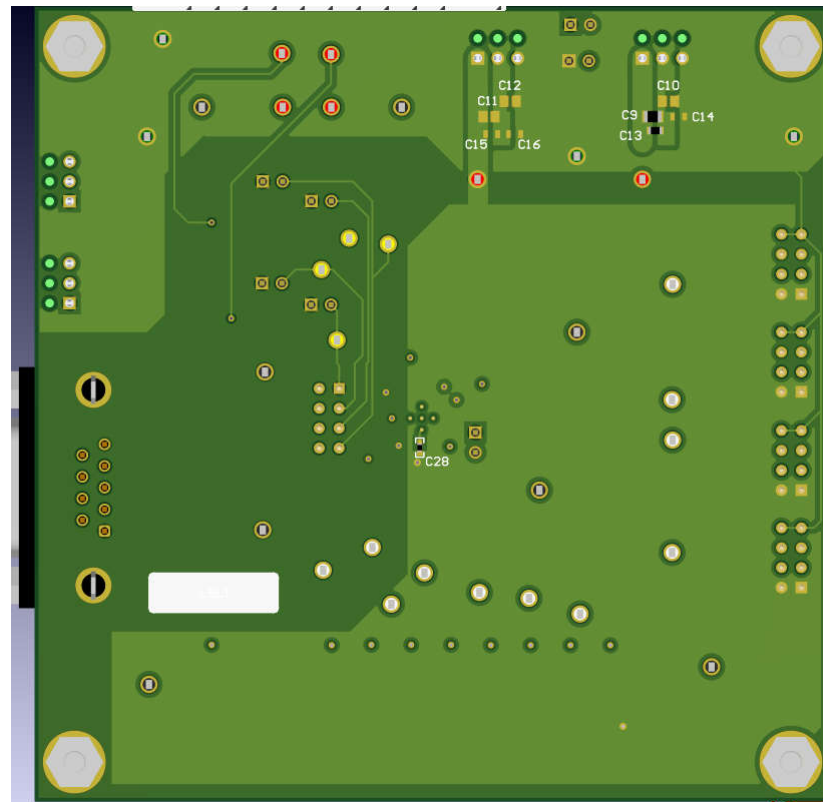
THVD4421EVM - 底层 3D PCB 布局
